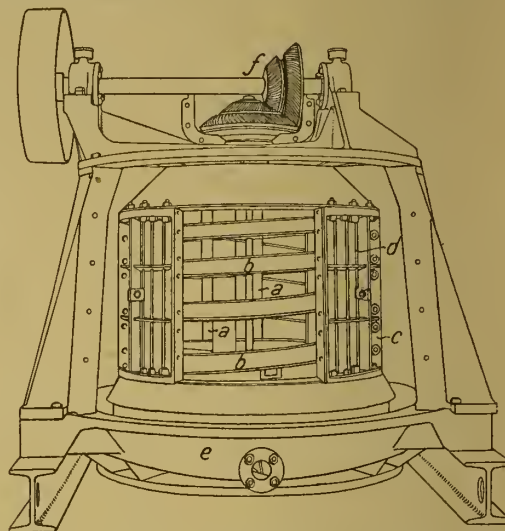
Ansicht der geöffneten Hoyle-Zentrifuge.
